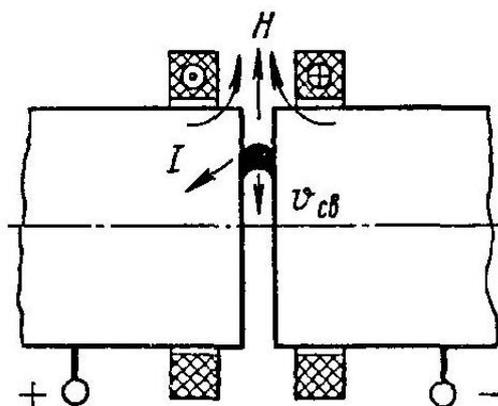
Схема сварки вращающейся «конусной» дугой
